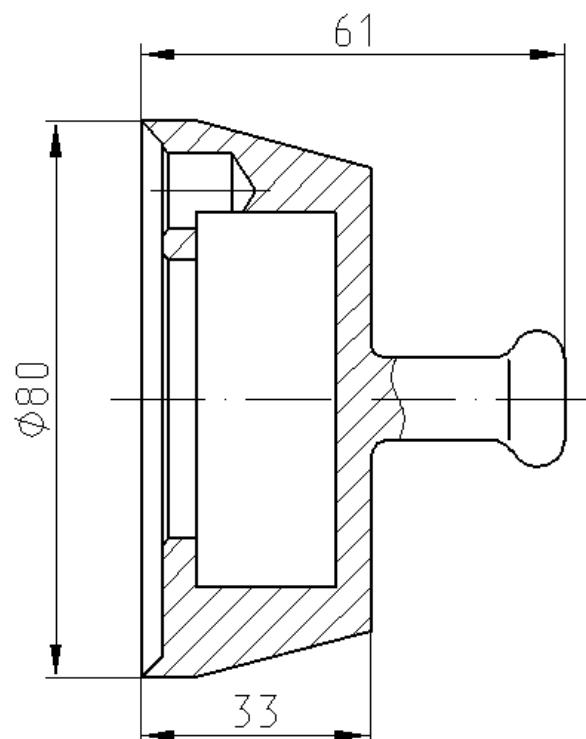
ЗМ 7853-4215, Оправка для установки сальникодержателя
